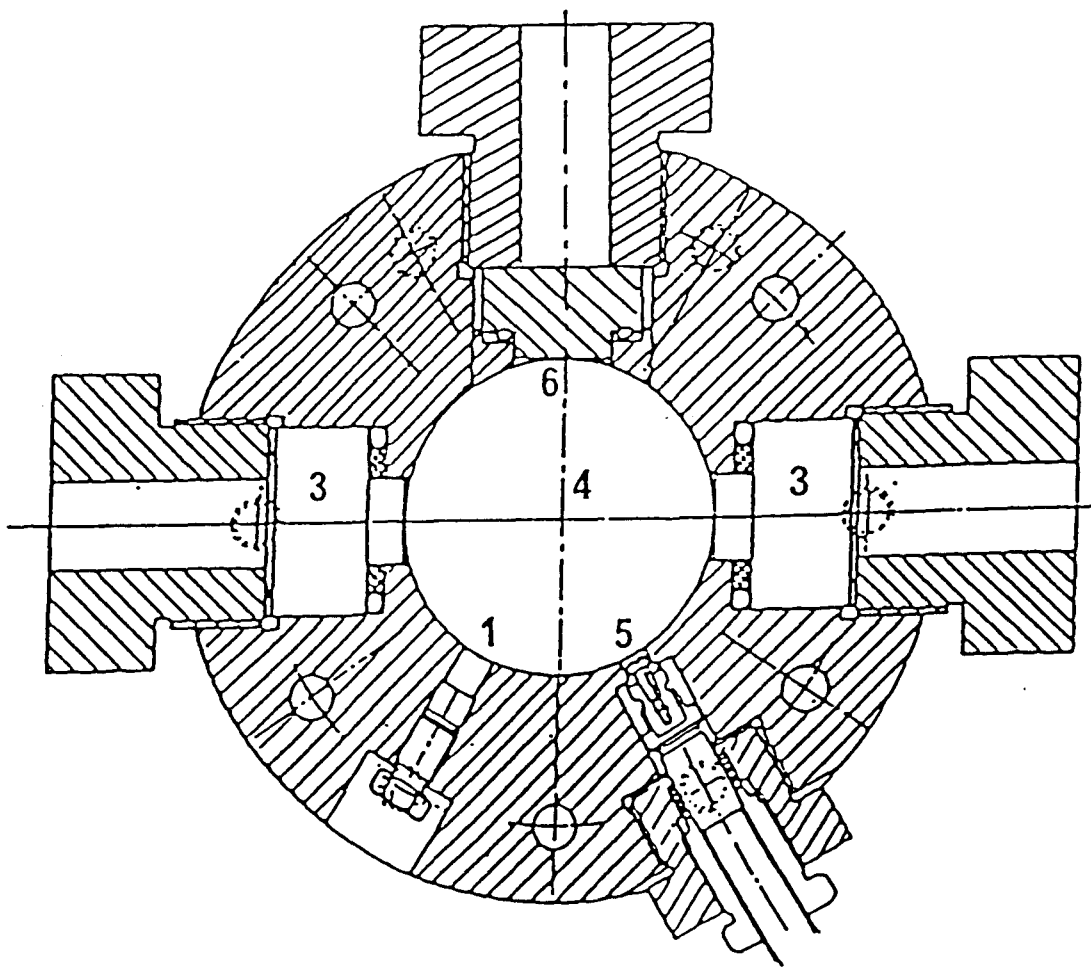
Coupe axiale de la chambre de combustion et du piston compresseur [22]
